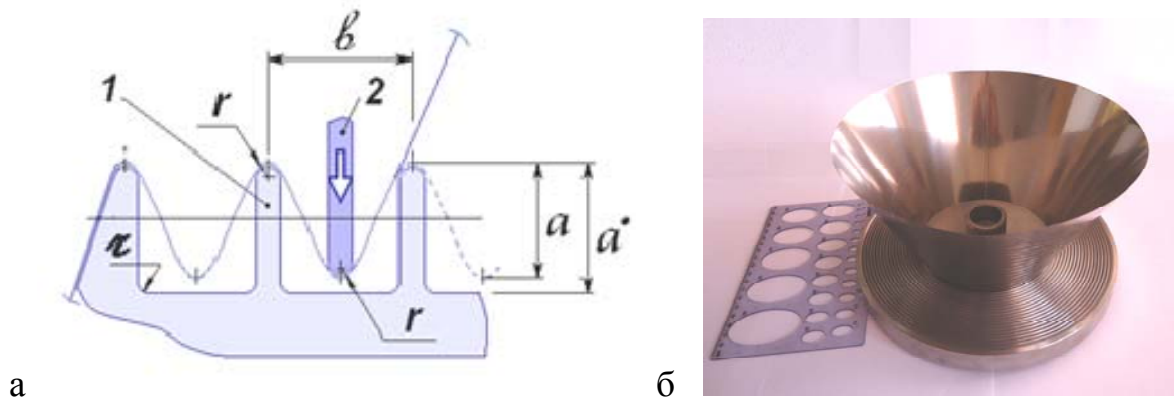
Розрахункова схема ротаційного пристосування (матриці) для згинання гладкою конічної заготовки (а) та дослідний зразок матриці (б); 1 - опорні ребра матриці, 2 – фрагмент формувального пуансона
